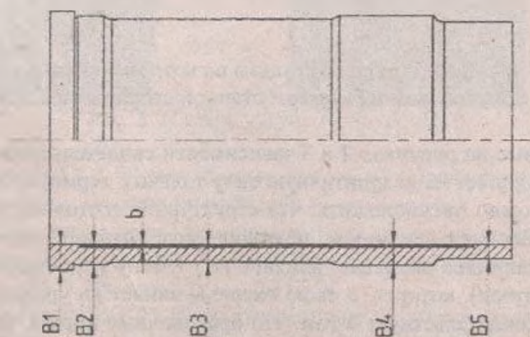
Схема гильзы цилиндра двигателя типа СМД.
